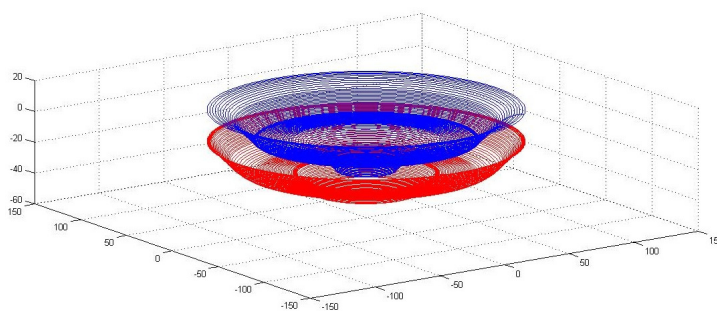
Werkzeugpfad gespiegelt an der Fläche
